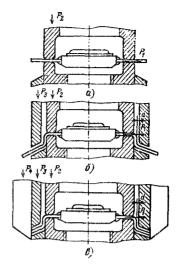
Конструкция штампа для формовки и обрезки выводов микросхем:
